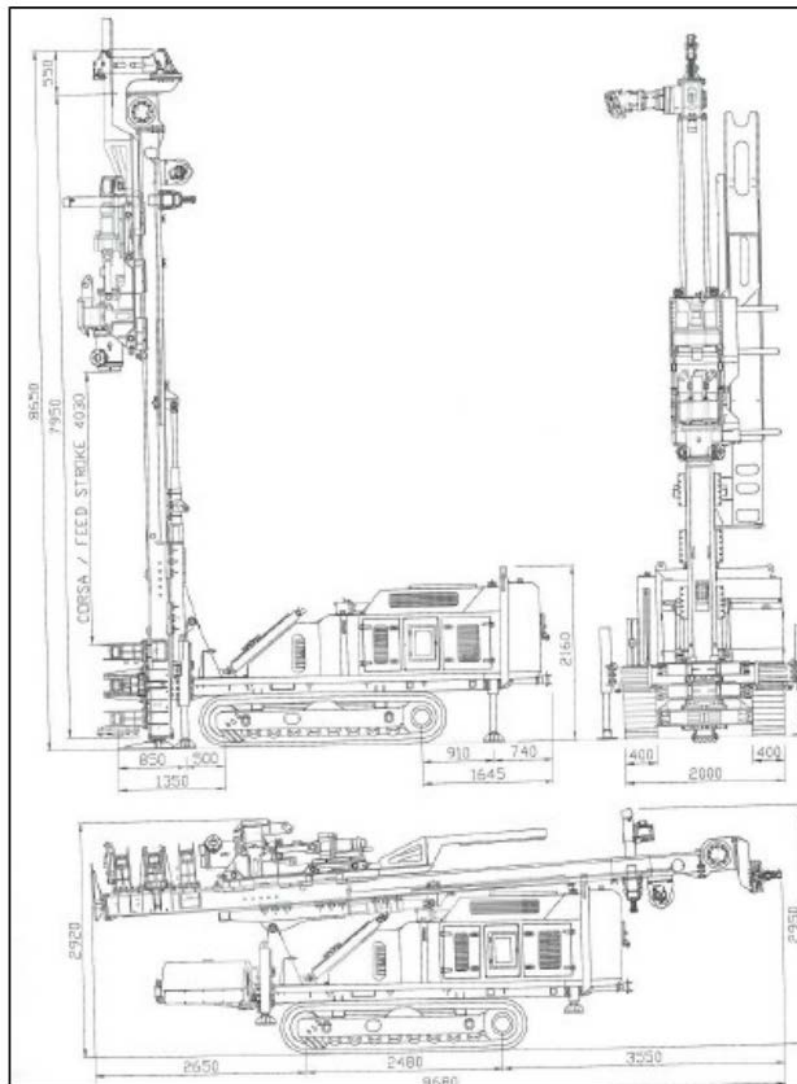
Dimensiones perforadora COMACCHIO MC900P. Fuente: comacchio.com [12]
